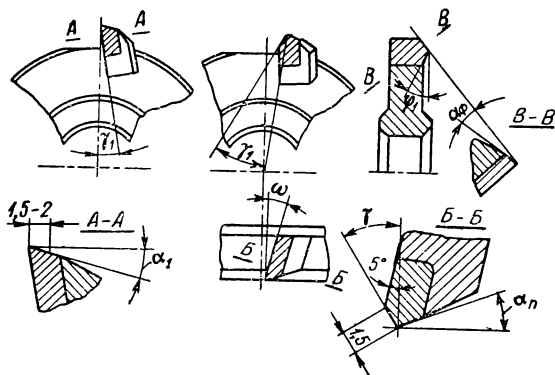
Геометрические параметры режущей части фрез из быстрорежущей стали.
